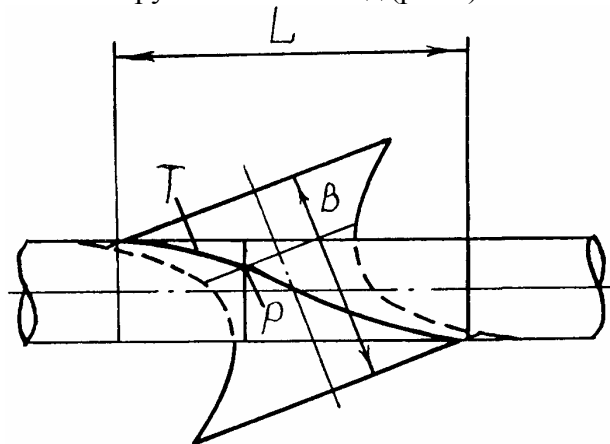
Способ обработки зубьев цилиндрического зубчатого колеса
